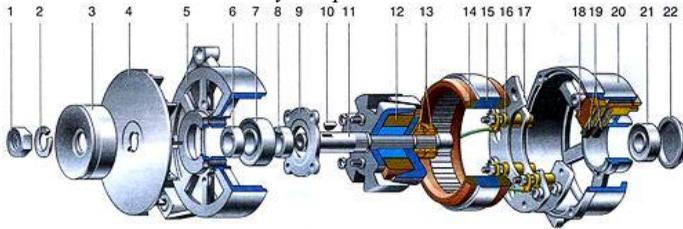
Генератор змінного струму: 1 - гайка шківів; 2 - шайба; 3 - шків; 4- крильчатка; 5 - передня кришка, 6, 8 - дистанційні втулки; 7- передній підшипник; 9- шайба; 10 - шпонка; 11 - вал ротора; 12 - ротор; 13 - контактні кільця; 14 -обмотка статора; 15 - статор; 16 - ізоляційна втулка діода випрямного блоку; 17 - пластина випрямного блоку; 18 - щітковий вузол; 19 - щітки; 20 - корпус регулятора напруги і щіткового вузла; 21 - задній підшипник; 22 - кришка заднього підшипника.
